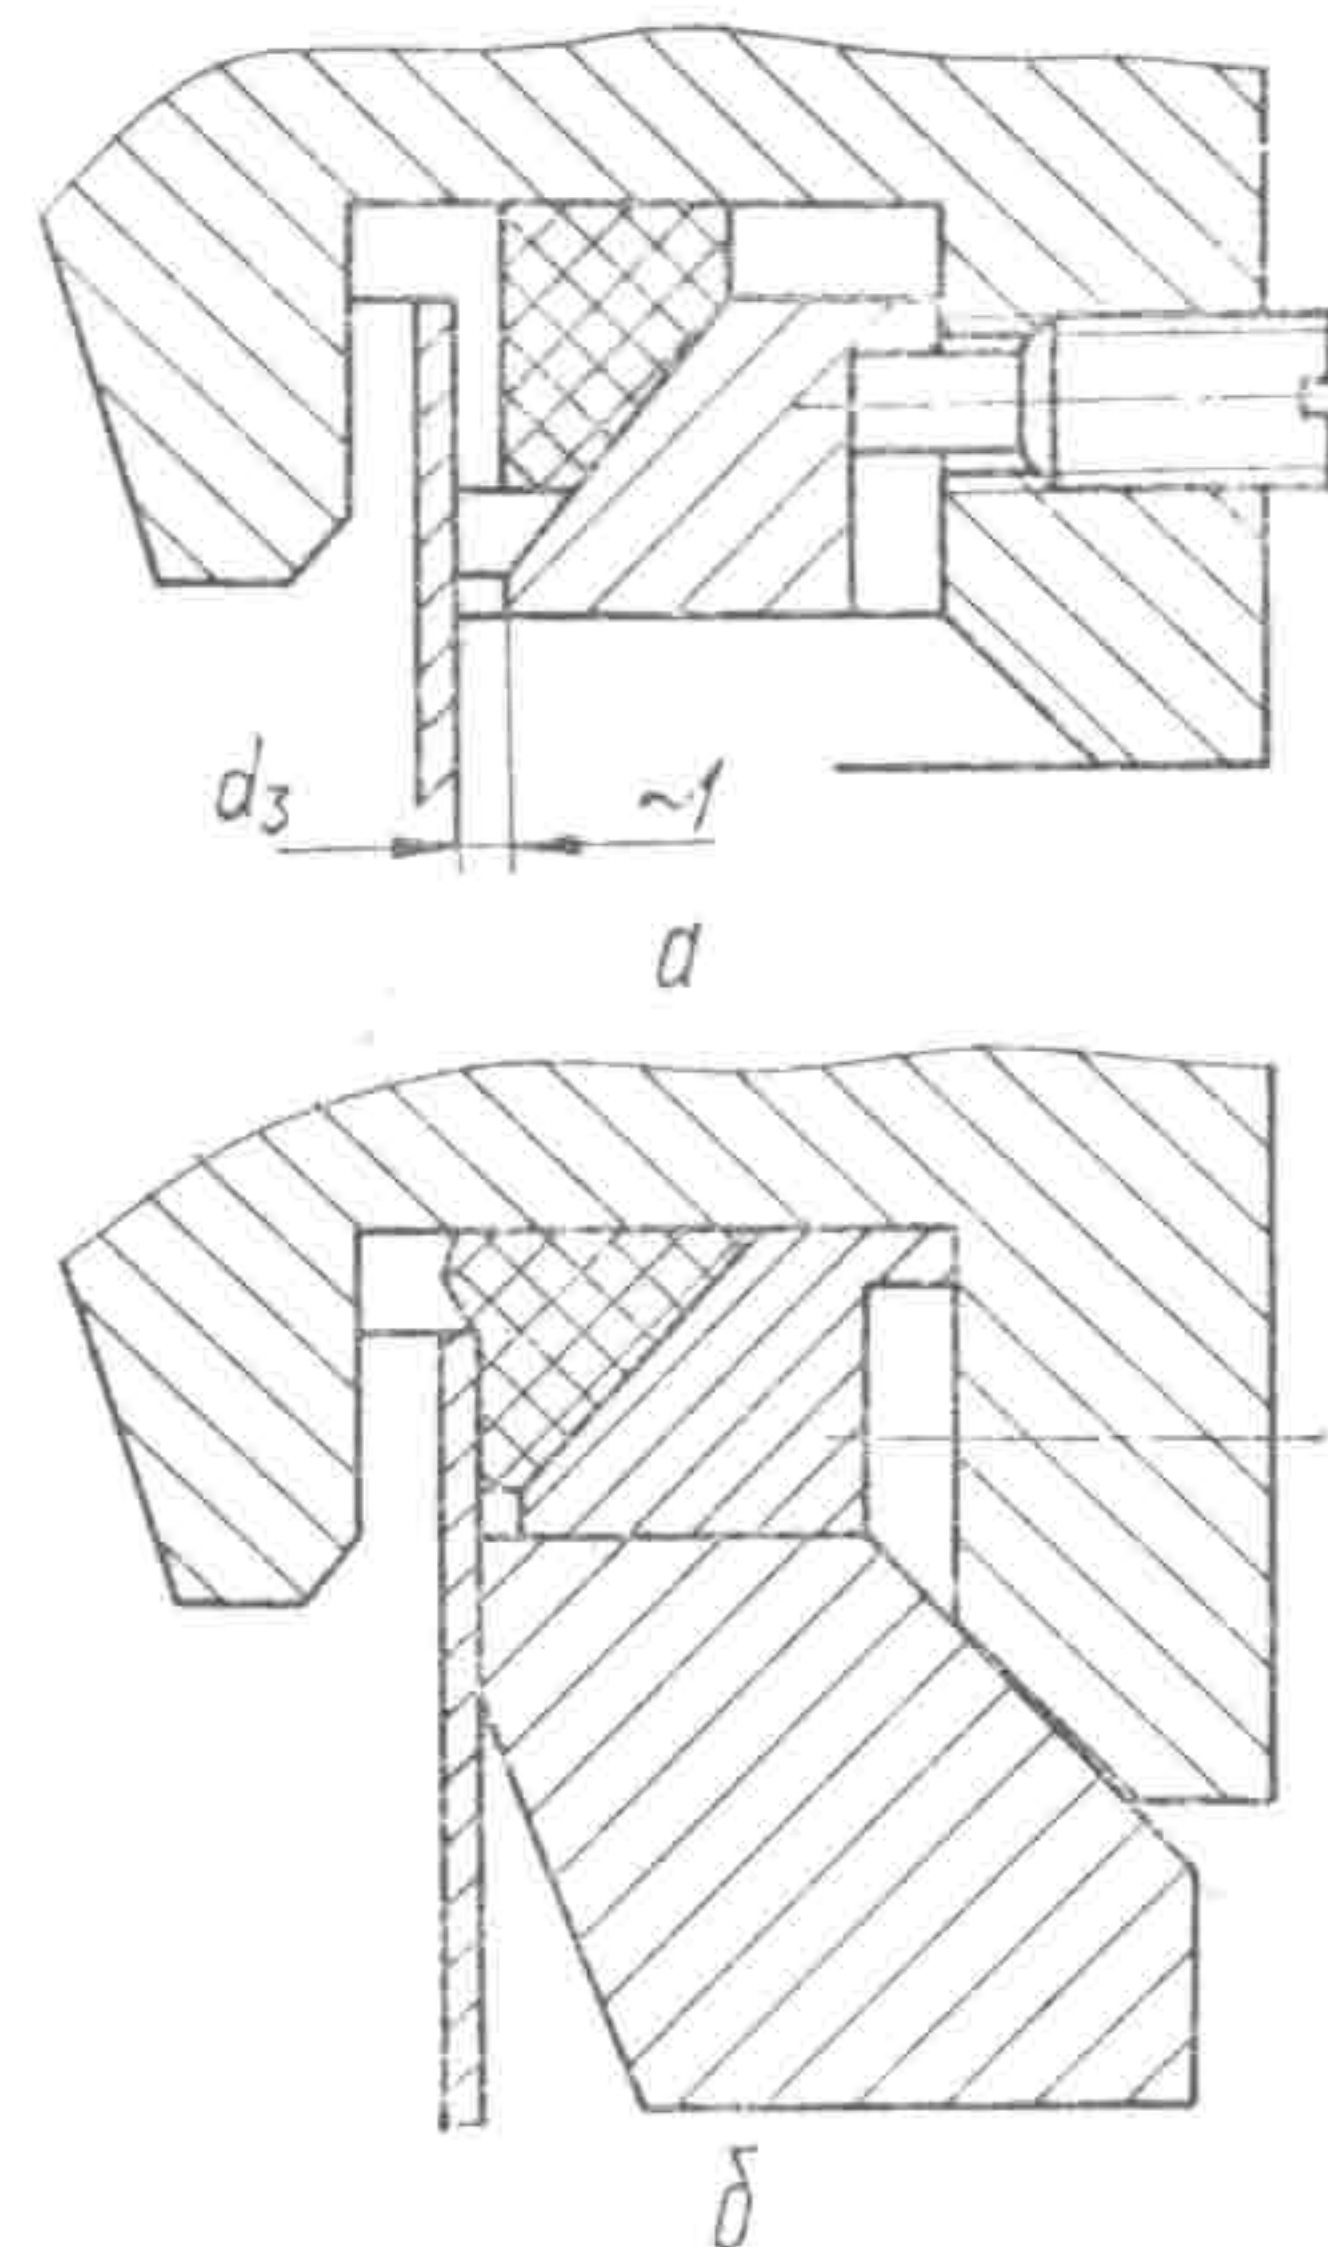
Уплотнение трубчатой заготовки при незажатой (а) и зажатой (б) оснастках
